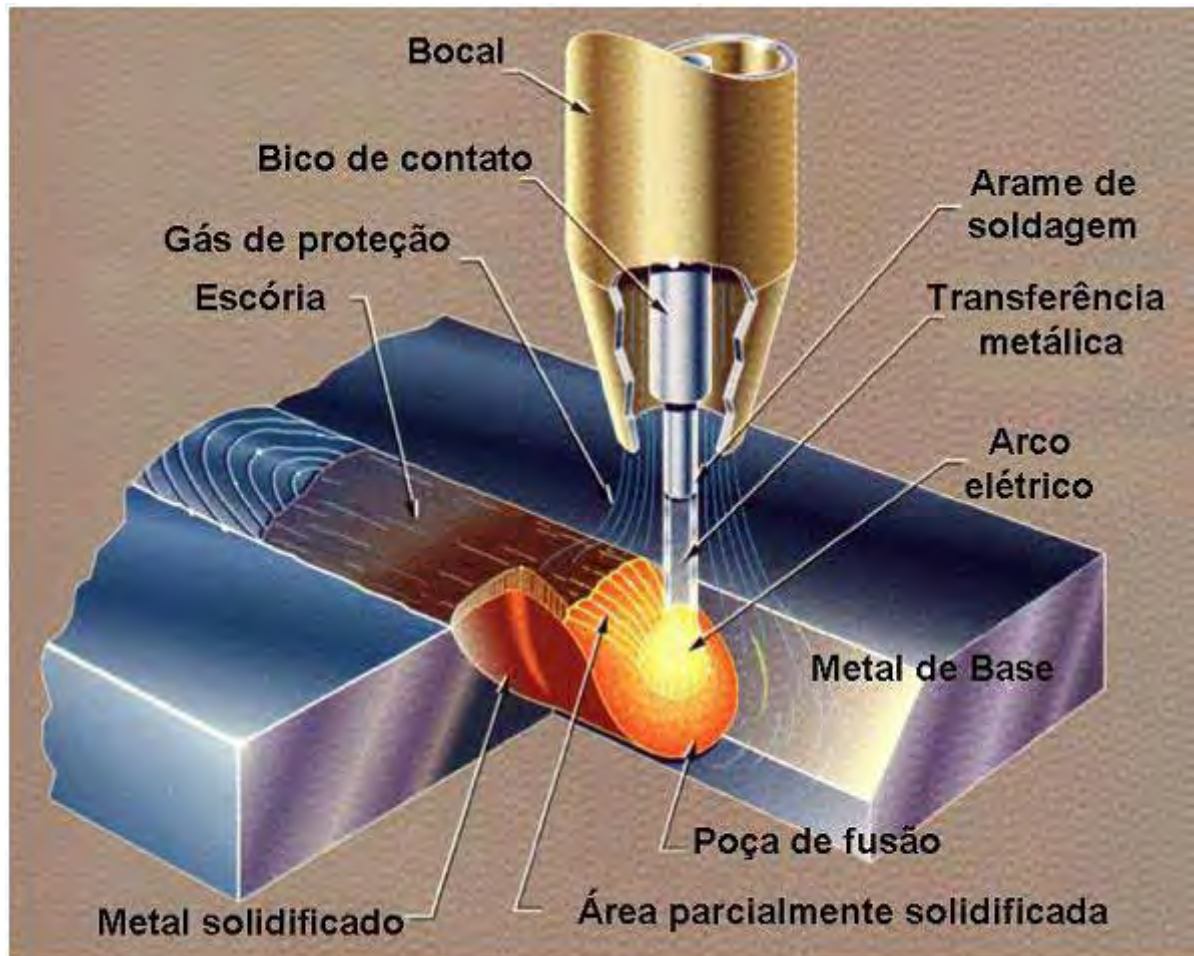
Processo de soldagem GMAW (COSTA, 2003).
